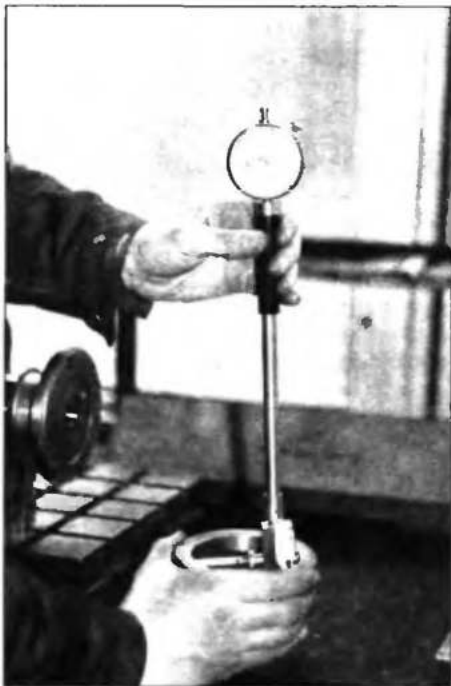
Настройка нутромера на нуль с помощью кольцевого калибра
